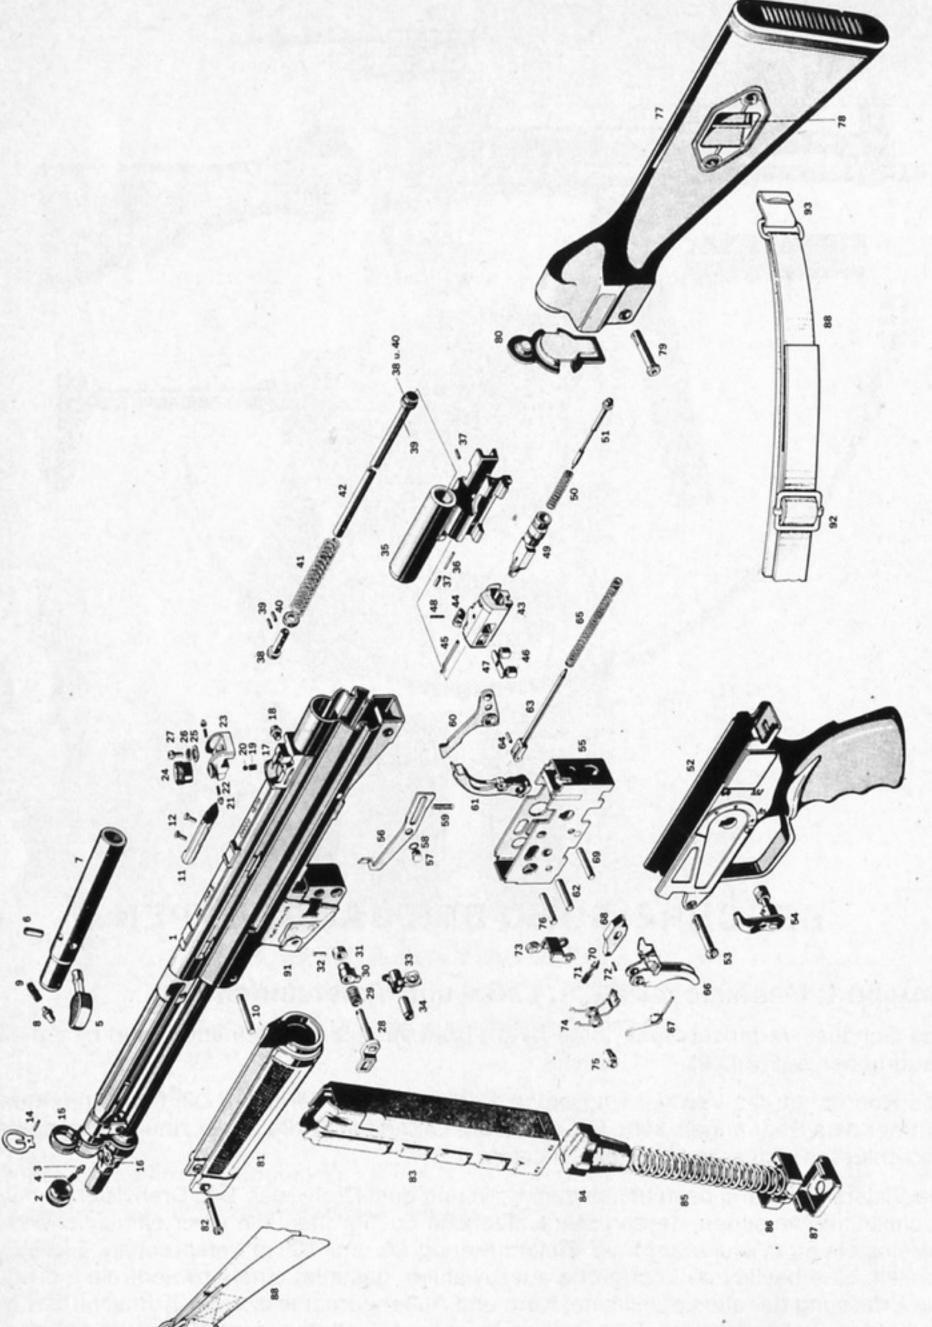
Explosionszeichnung der MP 5 A2 (Teileverzeichnis)
